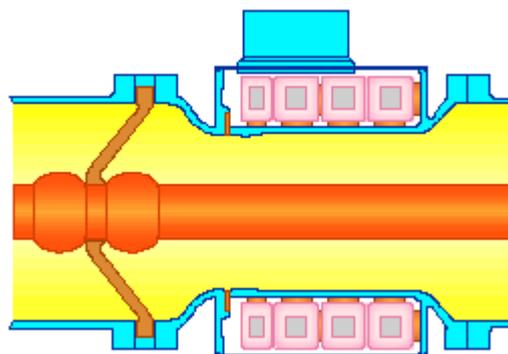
Трансформатор тока, установленный снаружи корпуса КРУЭ
